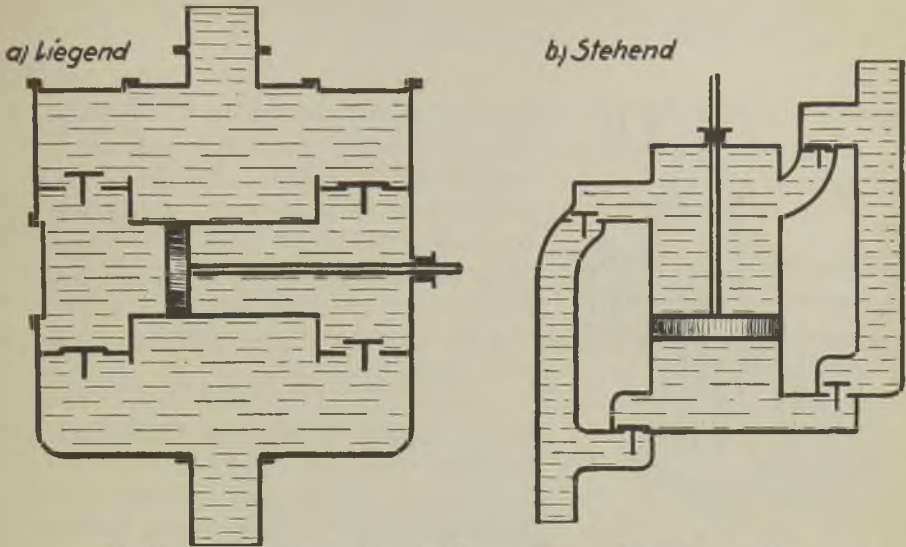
Doppelt wirkende Pumpen mit Scheibenkolben.
